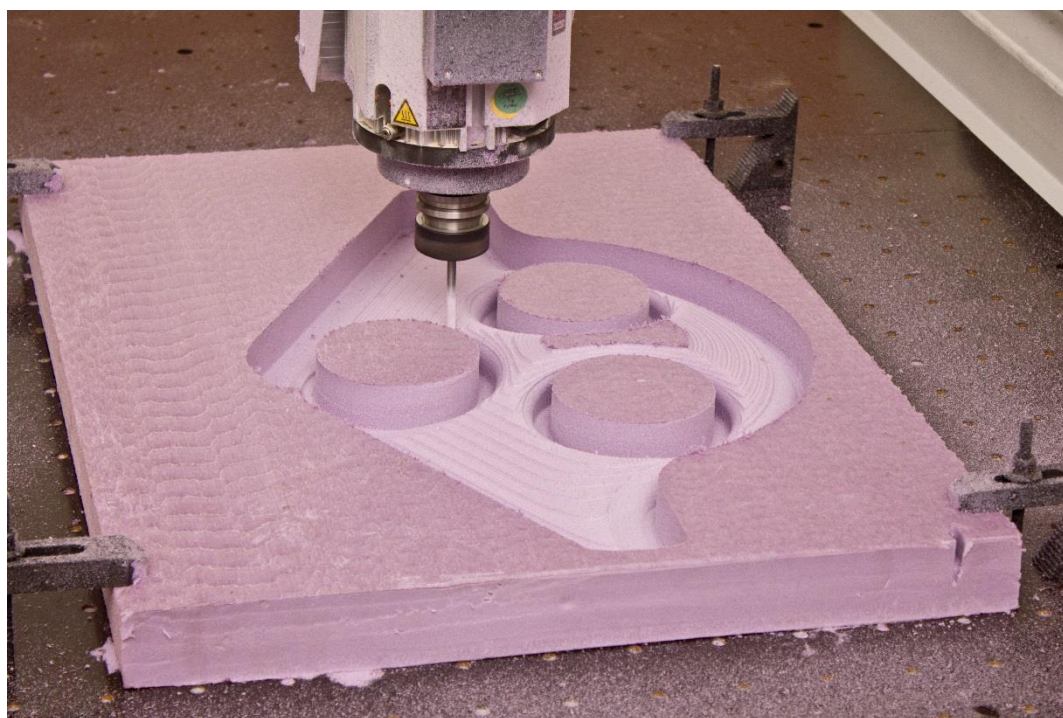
Изготовление основы болванки из пенопласта на станке ЧПУ
